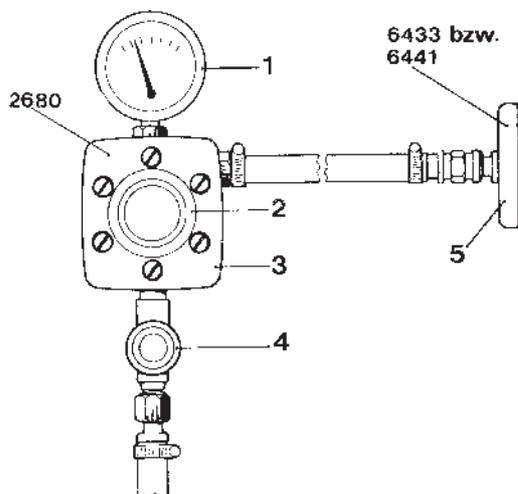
Appareil 2680 pour essai sous pression du système de refroidissement
